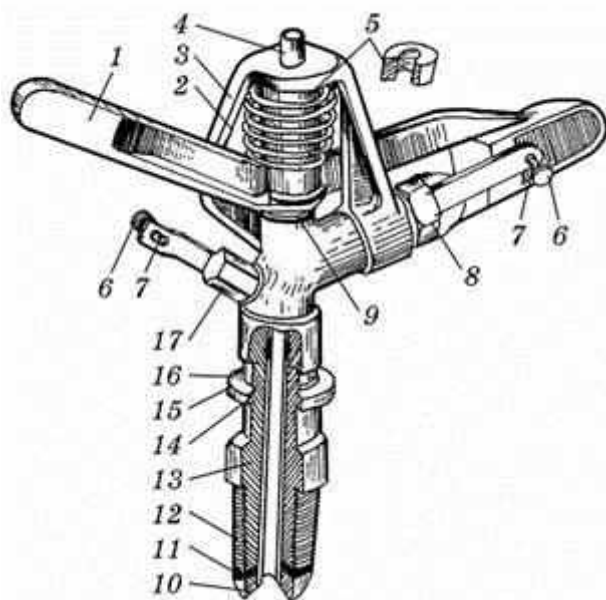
Далекоструминний дощувальний апарат з реактивною лопаткою:
